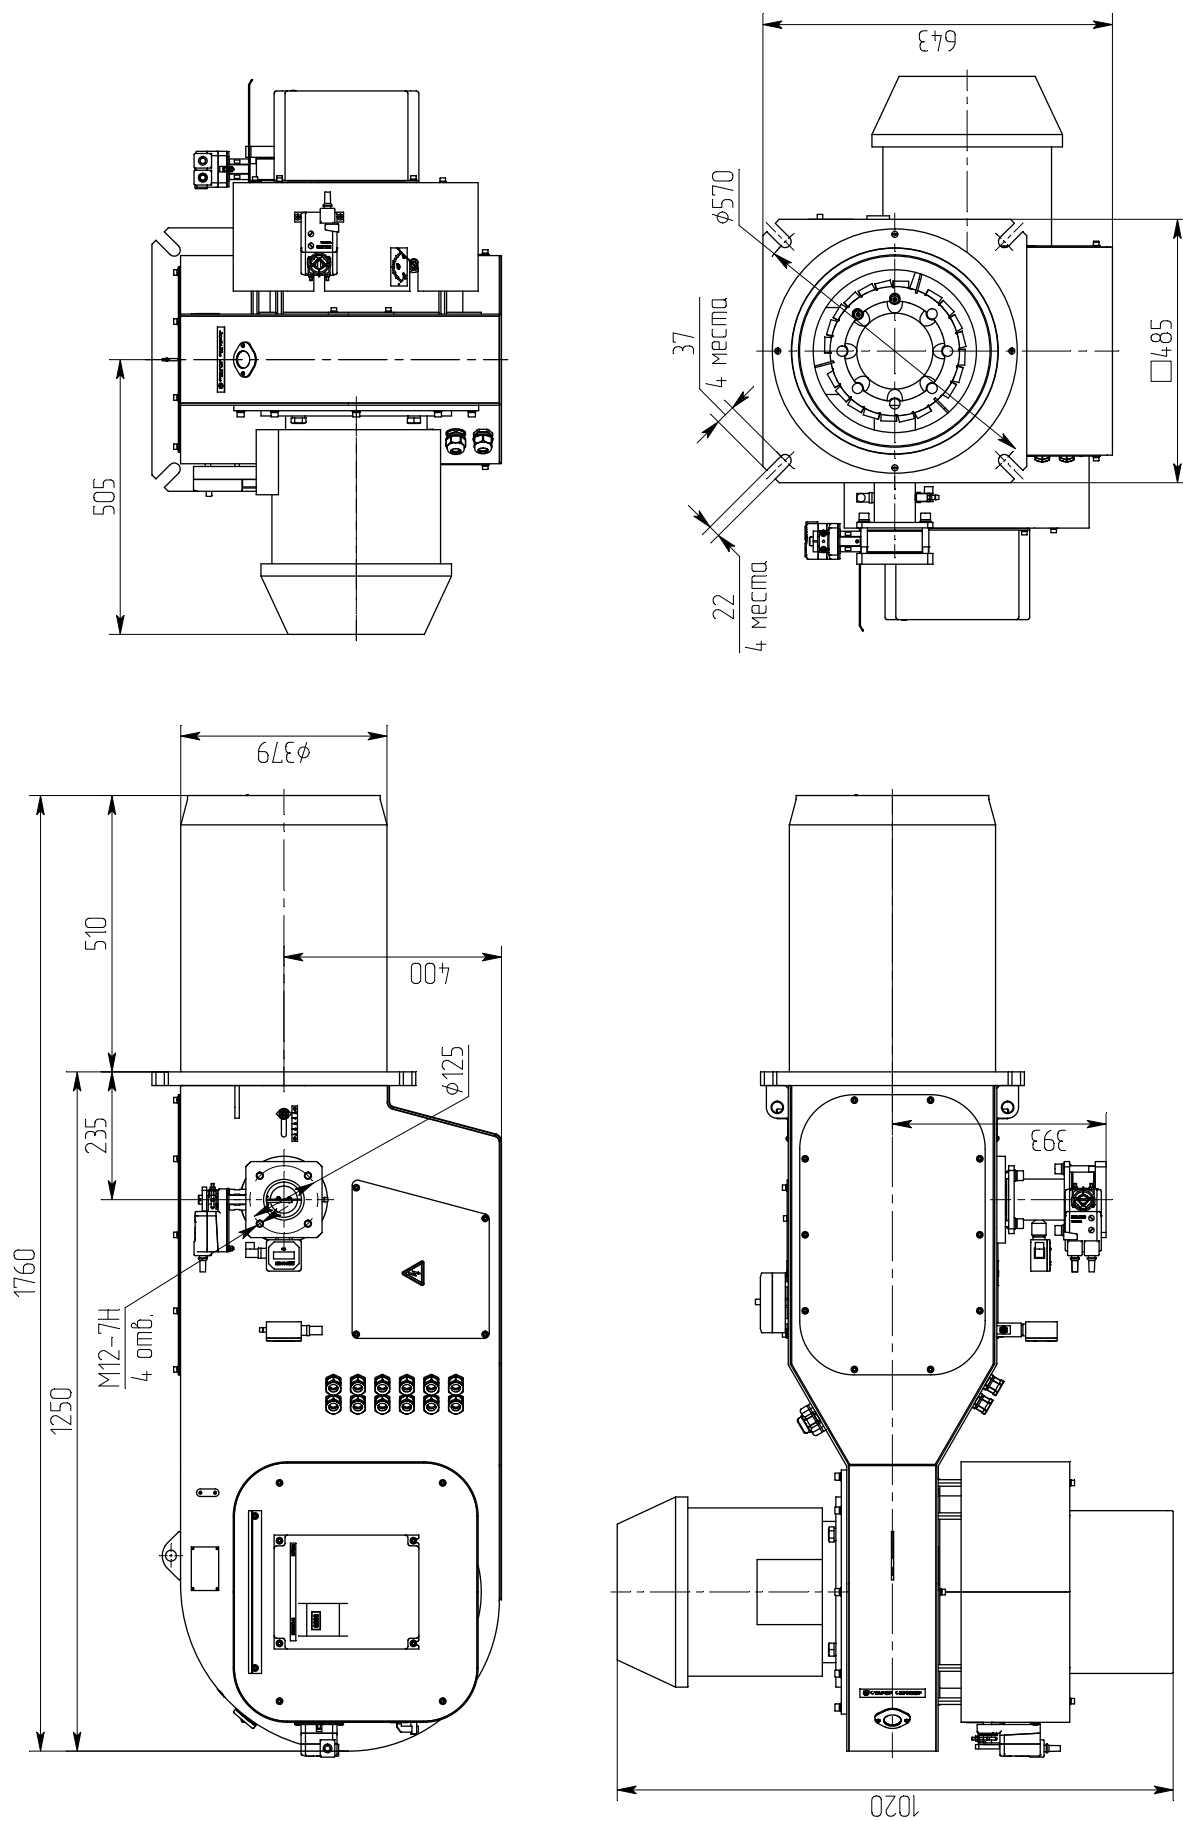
Габаритные и присоединительные размеры горелки (горелочного блока)
